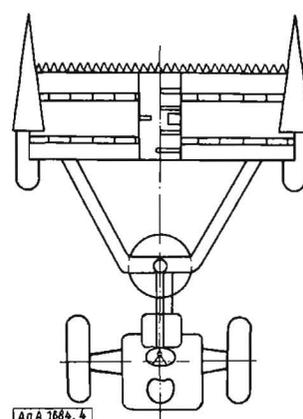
Frontmähbinder mit mittlerer Garbenablage
